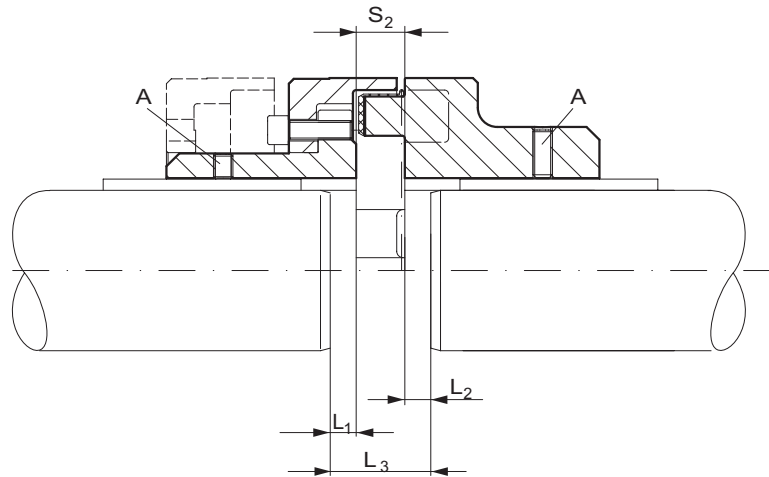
Установочные размеры муфты Nor-Mex на входном валу (сторона HSS) – адаптер двигателя 51672AXX
